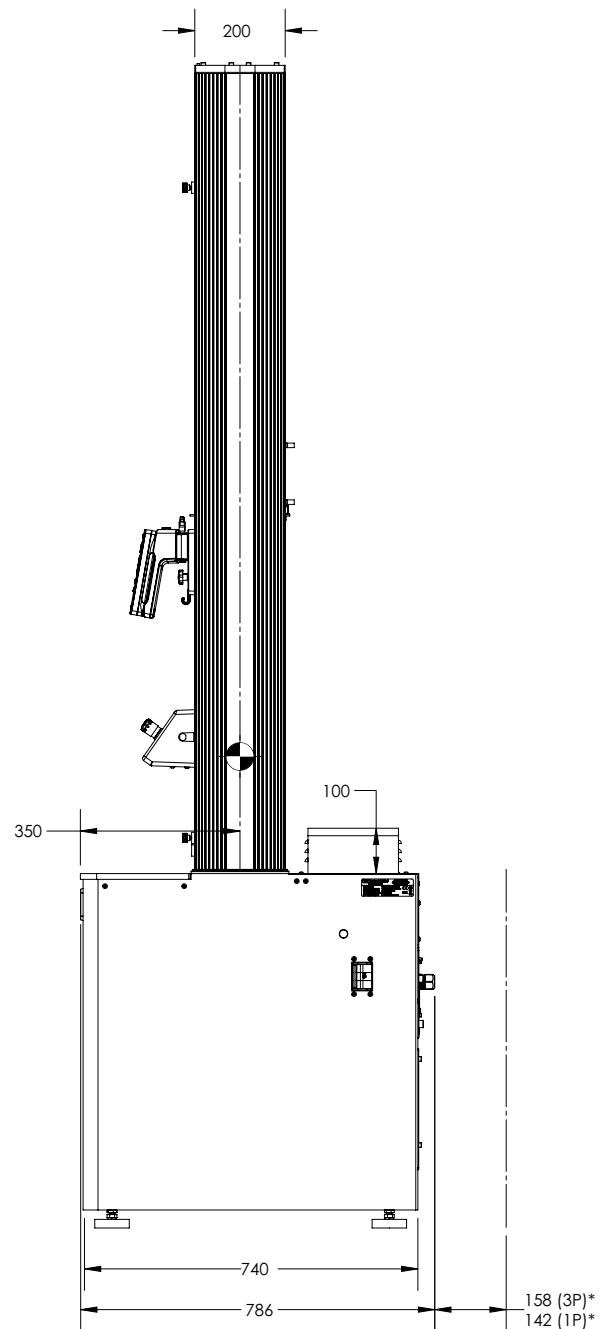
68FM-300 Prüfrahmendimensionen - Seitenansicht
